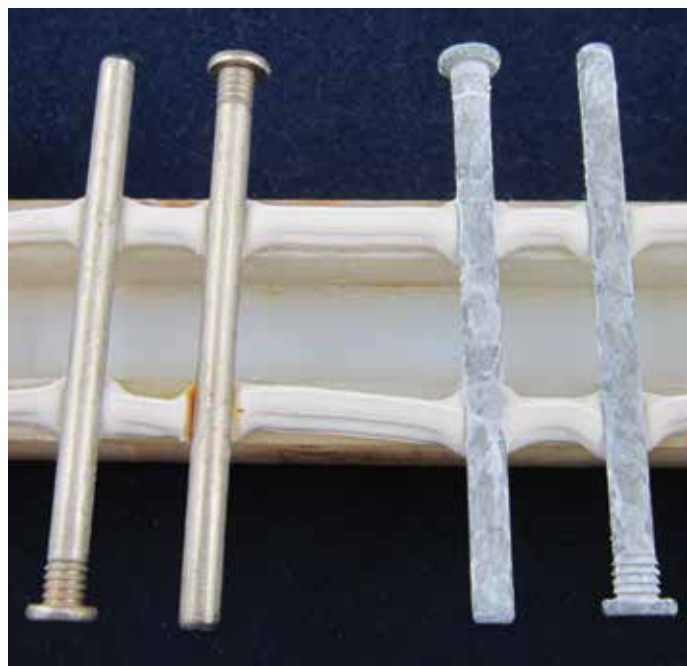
Nach dem Test bleiben die aus AISI 305 gefertigten Stifte unverändert (links), während die beschichteten Stifte (rechts) eine signifikante Weißrost aufweisen.
